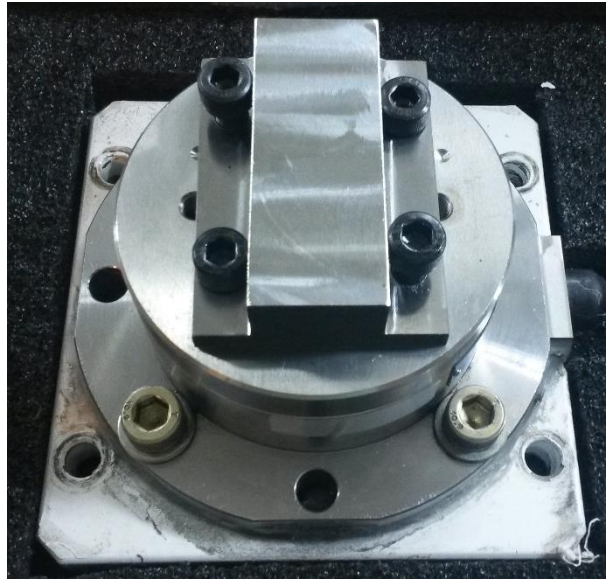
Corpo de prova para fresamento posicionado sobre a mesa do dinamômetro
